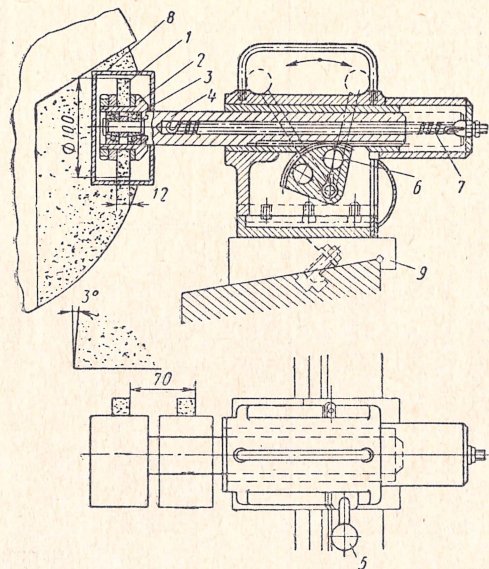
Специальное приспособление для безопасной правки торца круга на круглошлифовальном станке
